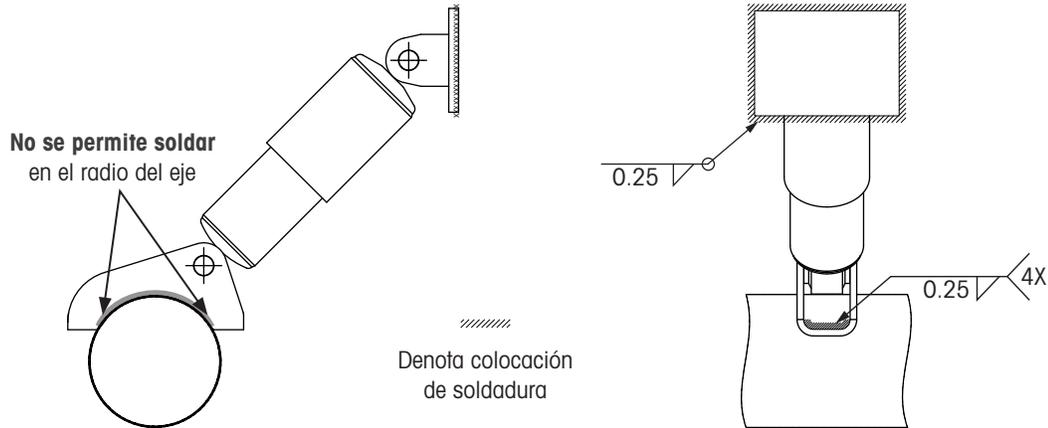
Especificaciones de soldadura de soporte de amortiguador remoto
